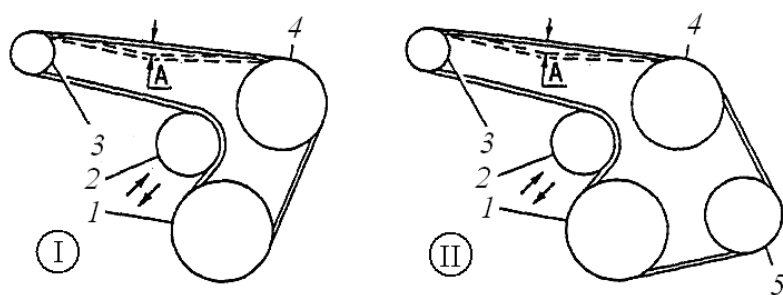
Схема натяжения ремня привода агрегатов: I – для автомобилей без гидроусилителя руля; II – для автомобилей с гидроусилителем руля; 1 – шкив коленчатого вала; 2 – натяжной ролик; 3 – шкив генератора; 4 – шкив водяного насоса; 5 – шкив насоса ГУР (для автомобилей с ГУР)
